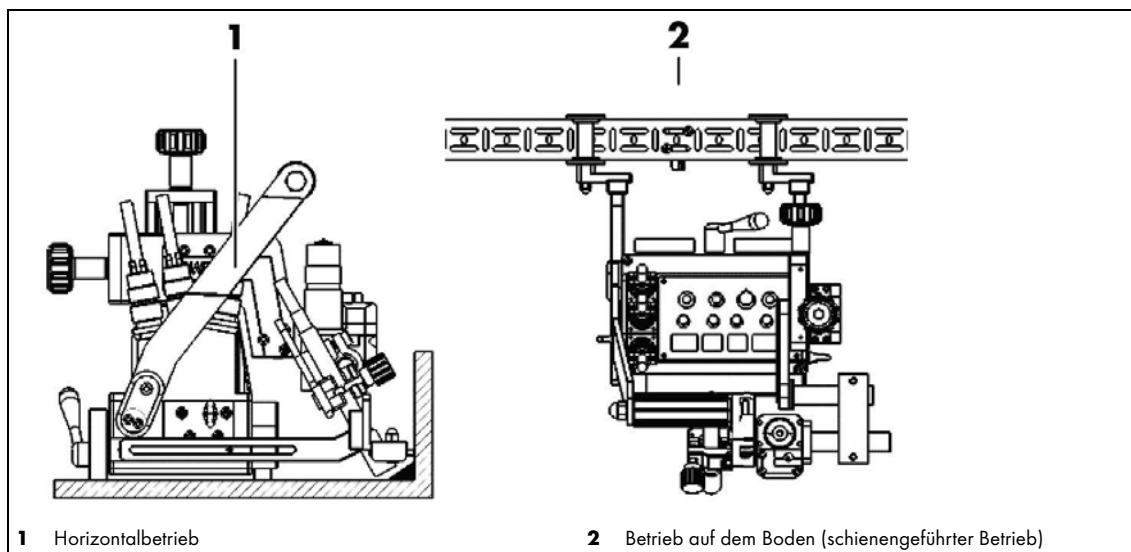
Einsatzmöglichkeiten des Schweißtraktors mit optionalem Zubehör
